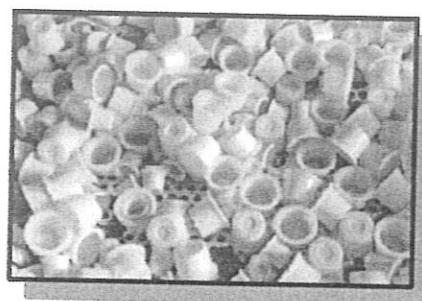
Sigilli di chiusura foro aspirazione carburante
